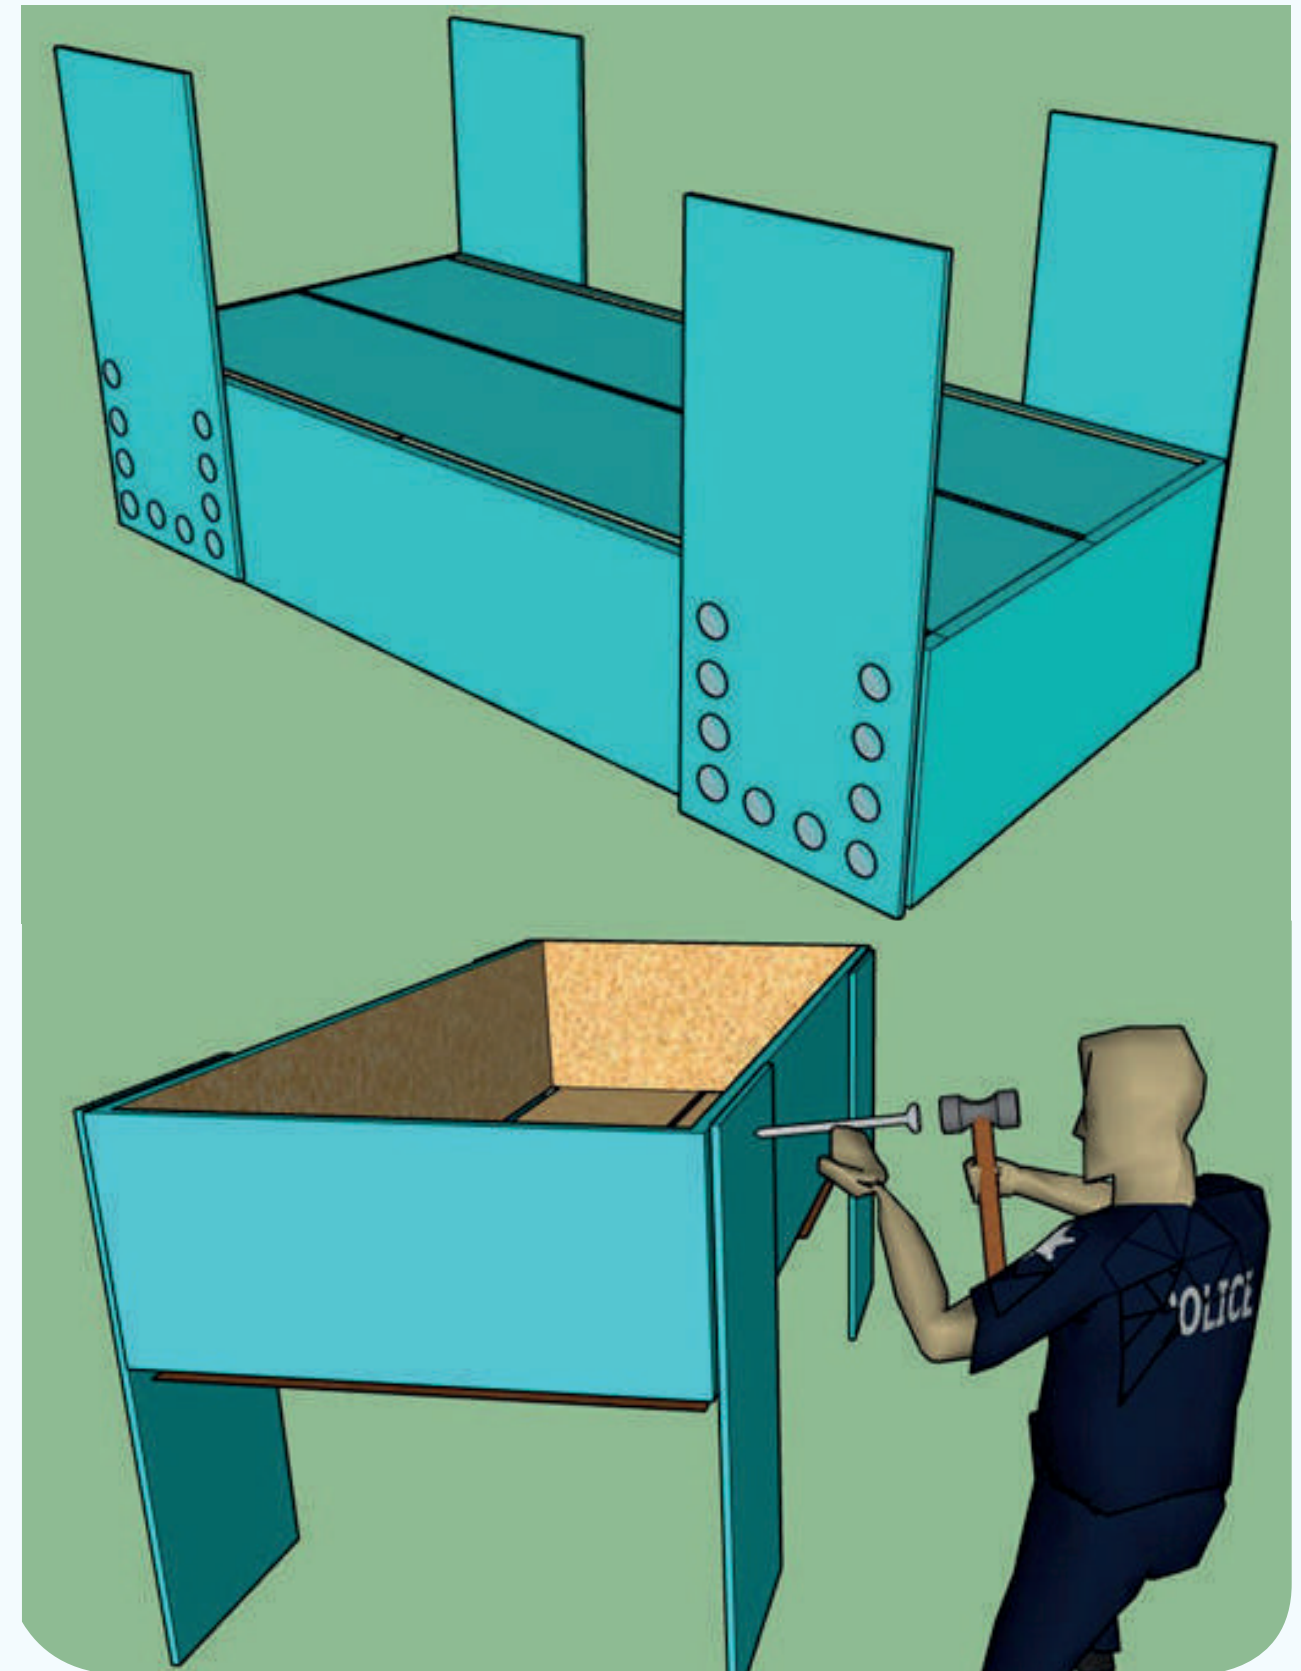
Elaboración de cama elevada. (Autora, 2018)
